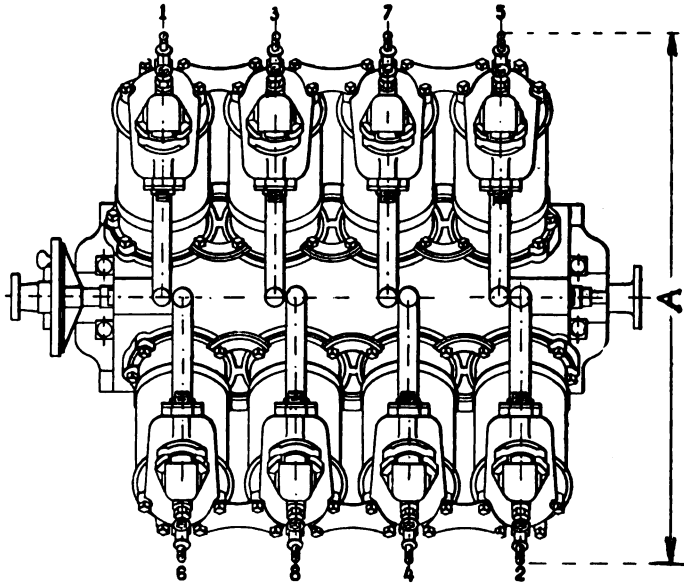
8 zylindriger Antoinette-Motor. Draufsicht.
